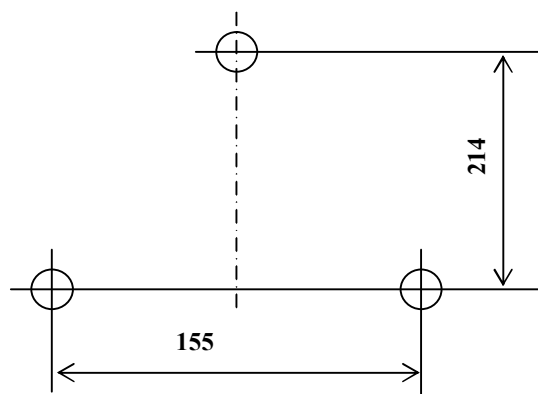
Схема разметки отверстий для крепления счетчиков
